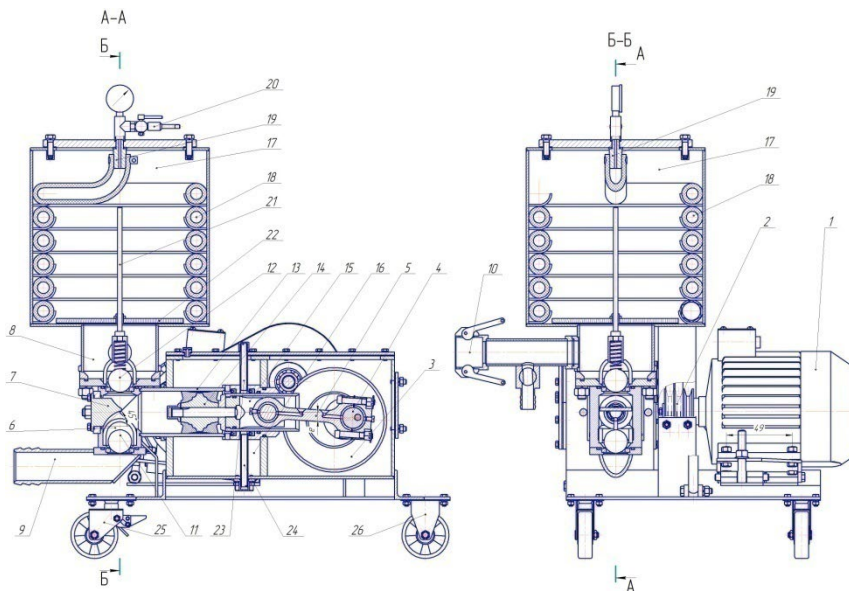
Однопоршневой растворонасос с комбинированным компенсатором увеличенного объёма: 1 – электродвигатель; 2 – клиноременная передача; 3 – одноступенчатый цилиндрический редуктор; 4 – кривошипный вал; 5 – кривошипно-шатунный механизм; 6 – всасывающая камера; 7 – цилиндрическая вставка; 8 – нагнетательная рабочая камера; 9, 10 – патрубки всасывающий и нагнетательный; 11, 12 – шаровые клапаны всасывающий и нагнетательный подпружиненный; 13 – рабочий цилиндр; 14 – поршень; 15 – ползун; 16 – штоковая полость; 17 – цилиндрическая камера; 18 – замкнутая камера; 19 – штуцер узла подкачки воздуха; 20 – ниппель; 21 – направляющий стержень; 22 – поплавкоограничитель; 23, 24 – каналные патрубки; 25, 26 – пара колёс.
